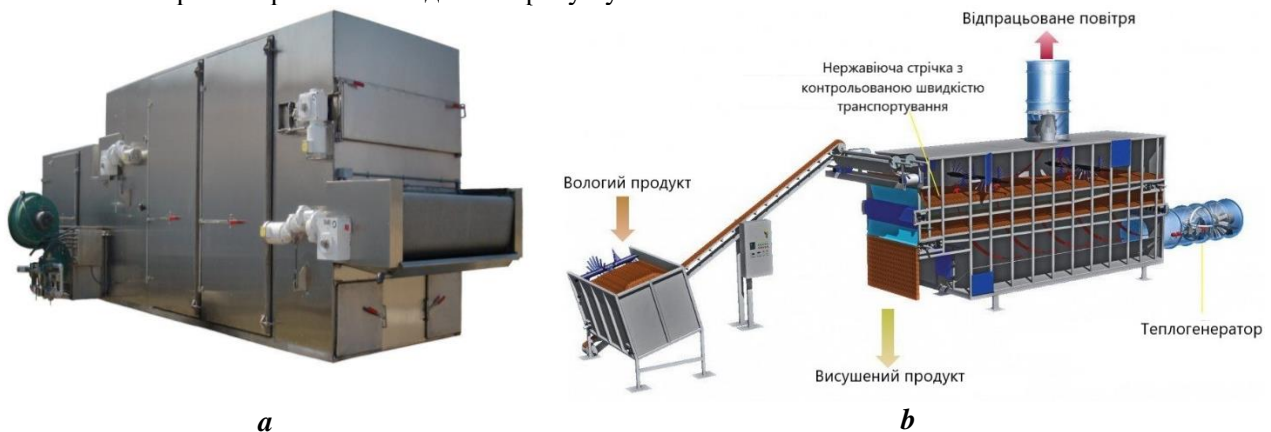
Загальний вигляд (а) і конструктивно-технологічна схема (б) стрічкової сушарки [20]
